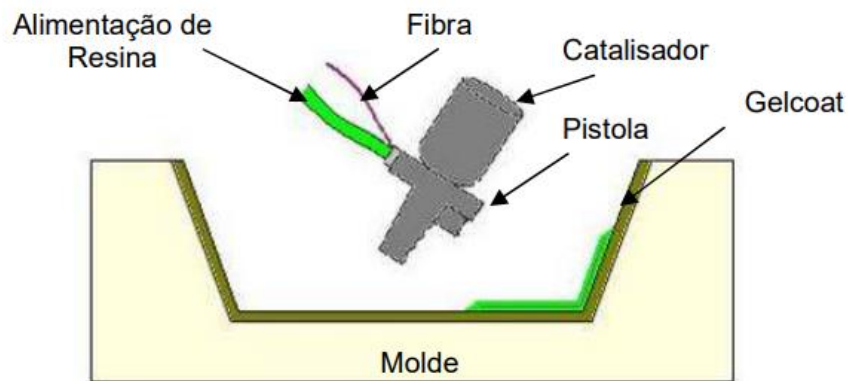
Moldagem por Spray Up (Franco, 2008).
